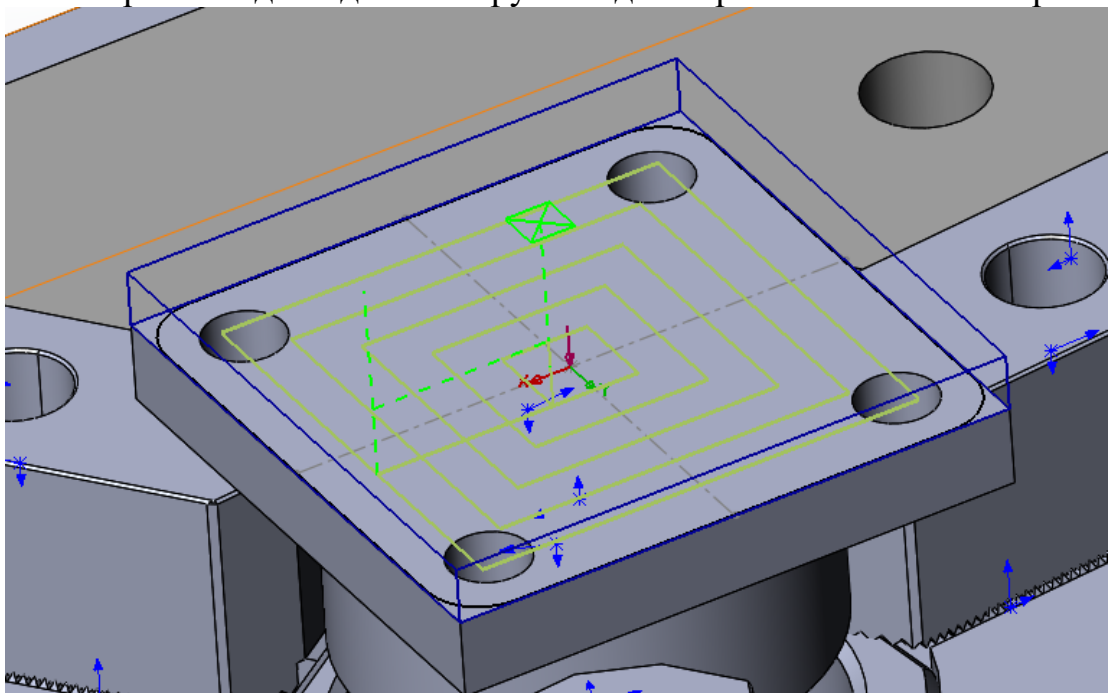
Траєкторія чорнвої обробки поверхні 5 на фрезерному верстаті
